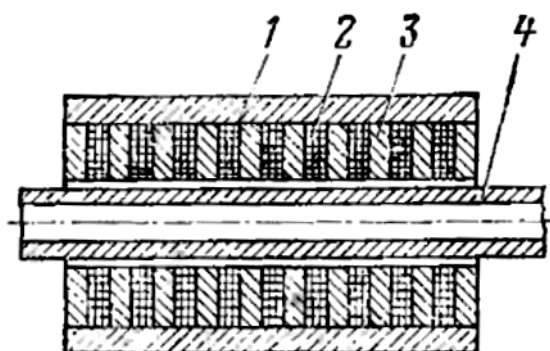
Трубчатый (коаксиальный) линейный двигатель
